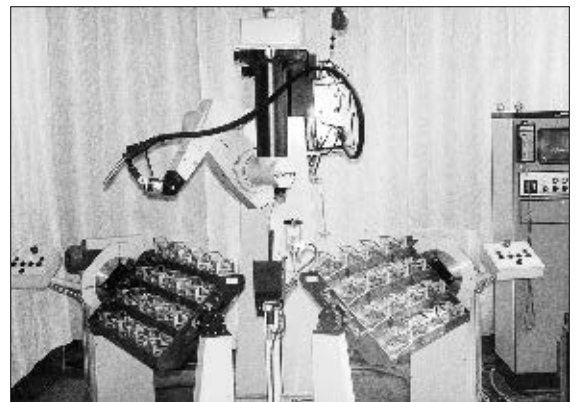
РТК дуговой сварки изделия «лодочка»
